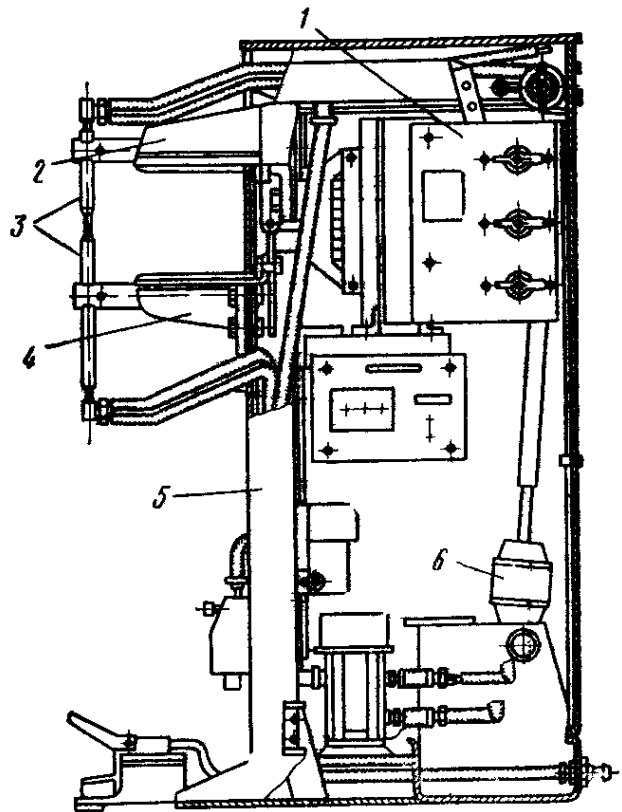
Машина для точечной сварки МТ-601.
